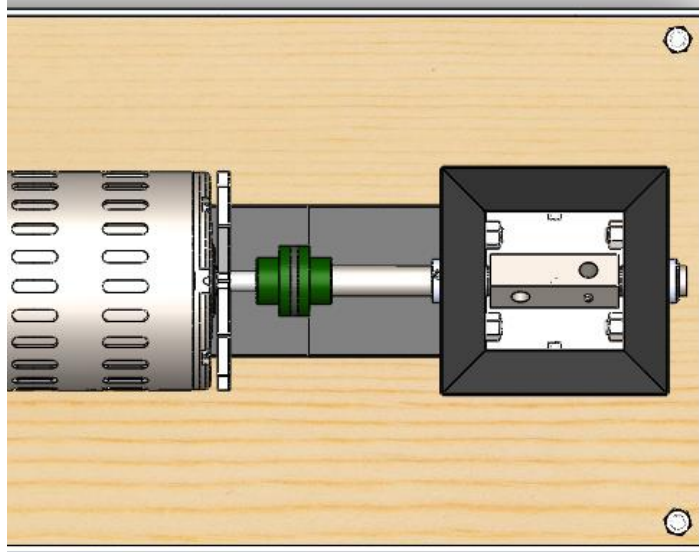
Detalle del eje, vista superior del equipo.
